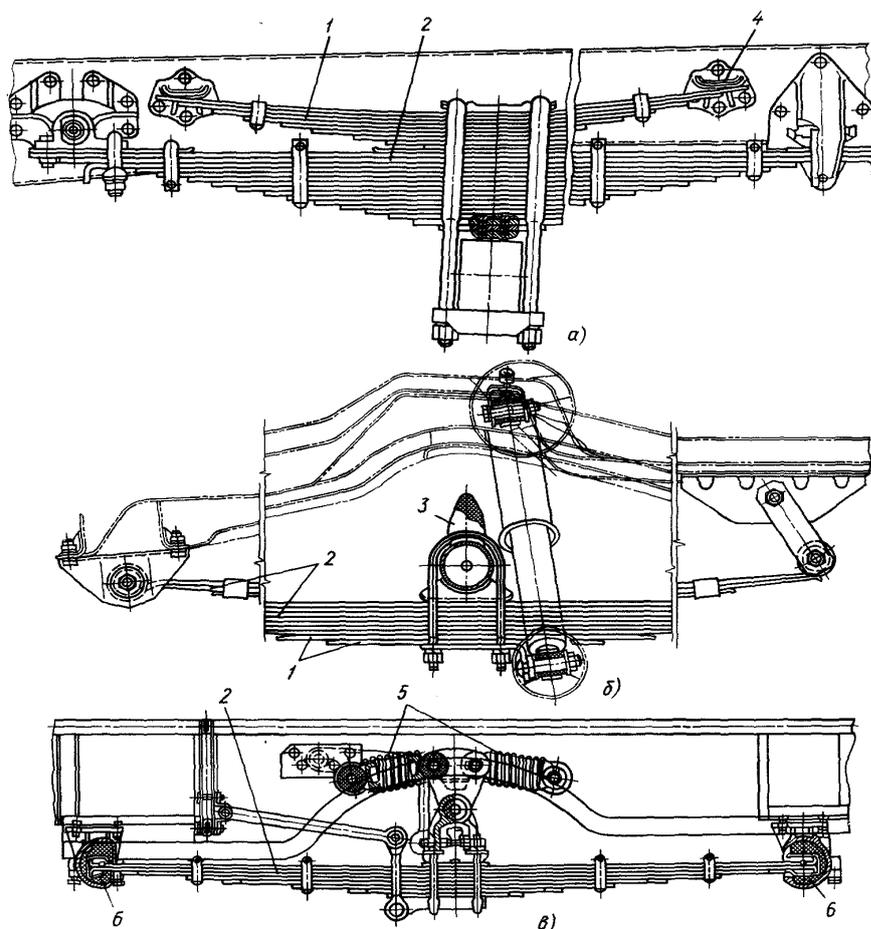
Рессорные подвески с дополнительными упругими элементами:
